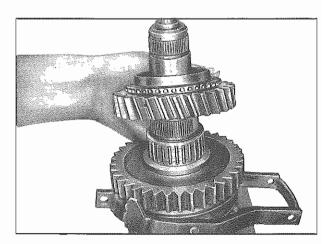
Ingranaggio della 2a marcia 2nd gear
